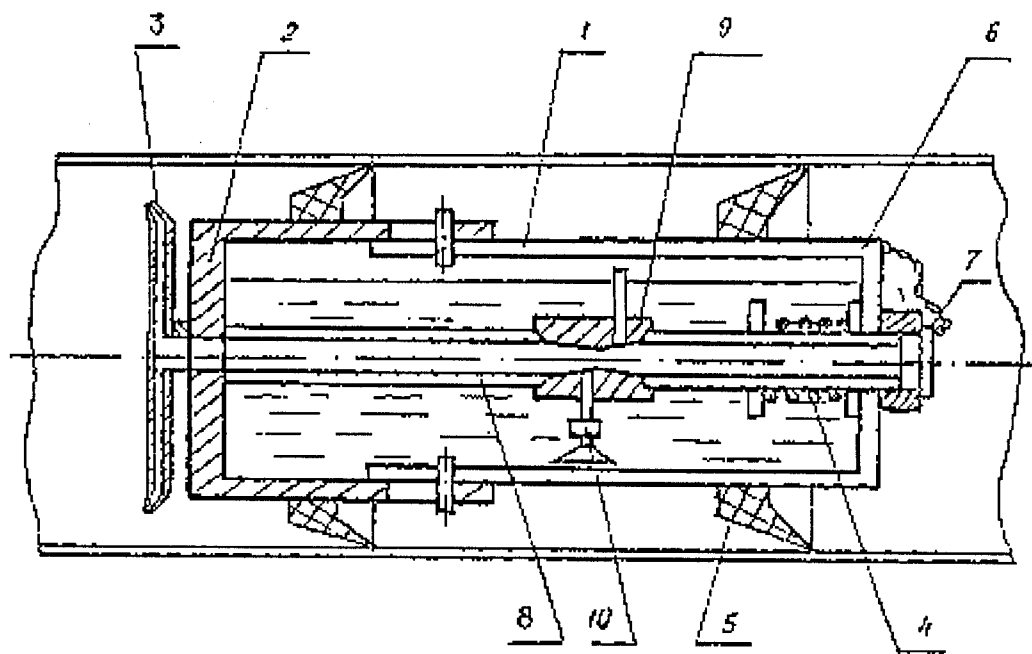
Принципова схема очисного пристрою нової конструкції
